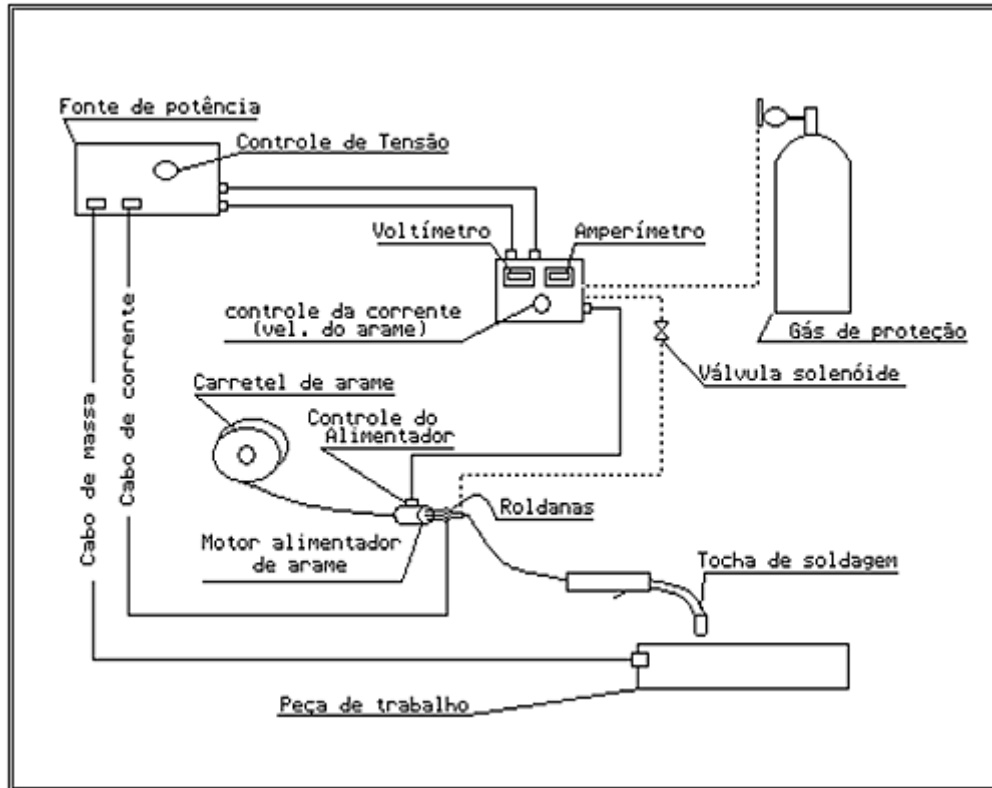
Equipamento básico para soldagem com arames Tubular [AWS, 1991]
